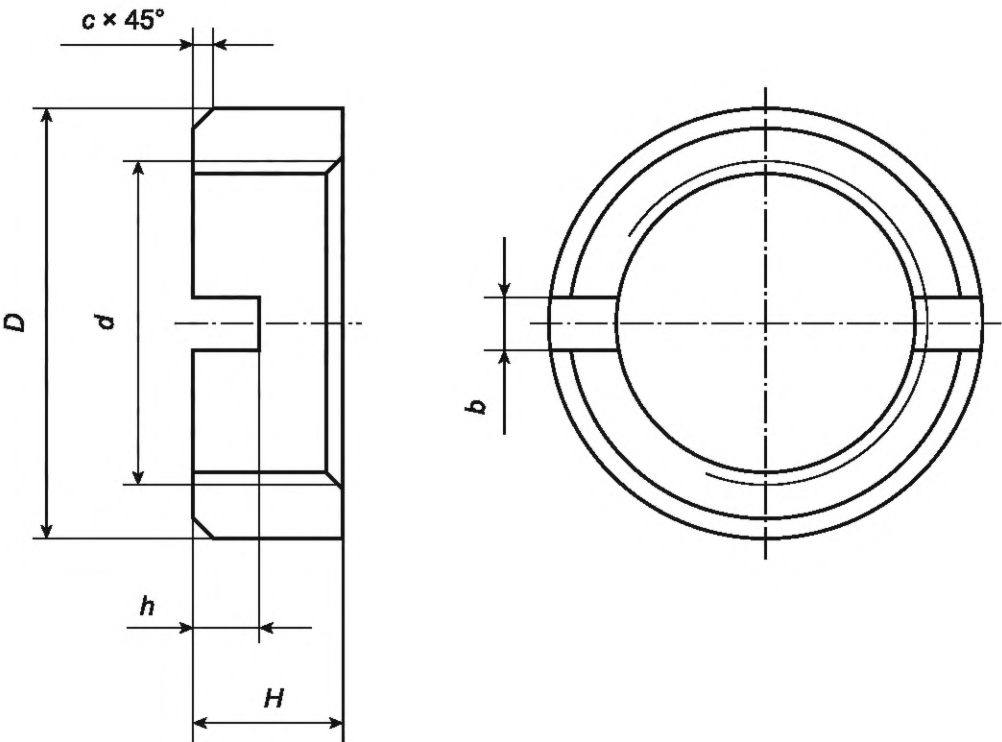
Конструкция круглых низких гаек со шлицем
